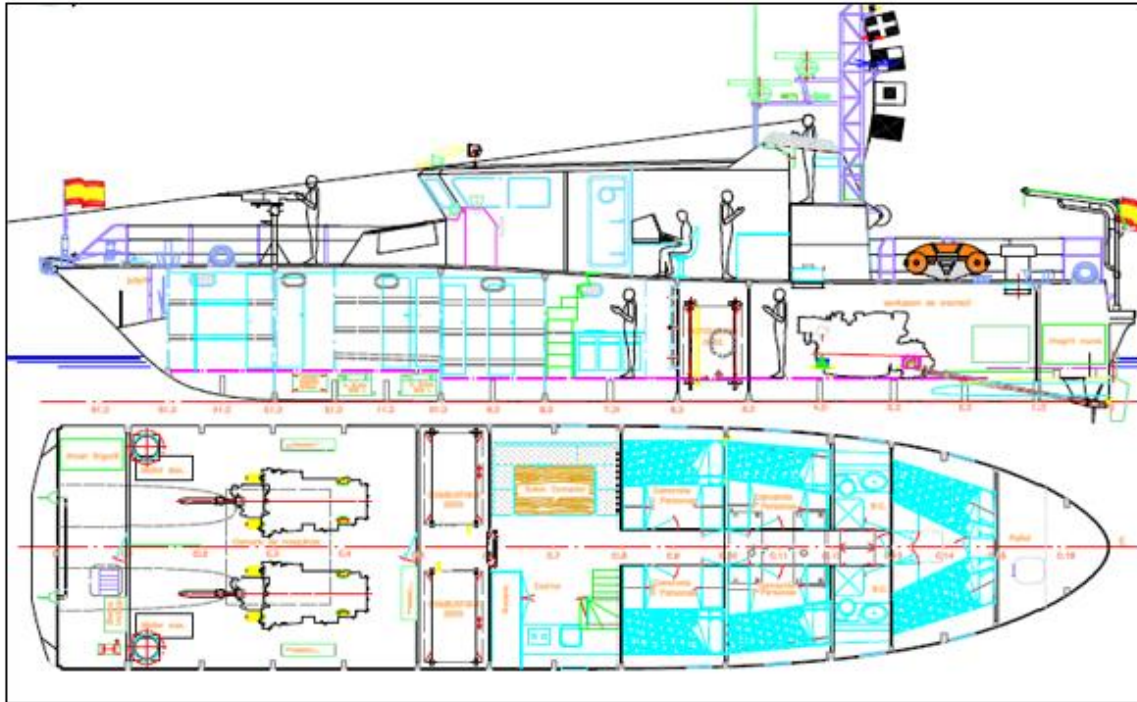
Plano de la Lancha de Instrucción Rodman66. [8]
